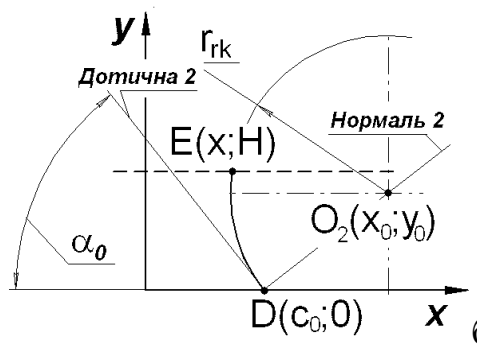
Теоретичний профіль робочої частини ножа-лопати:
